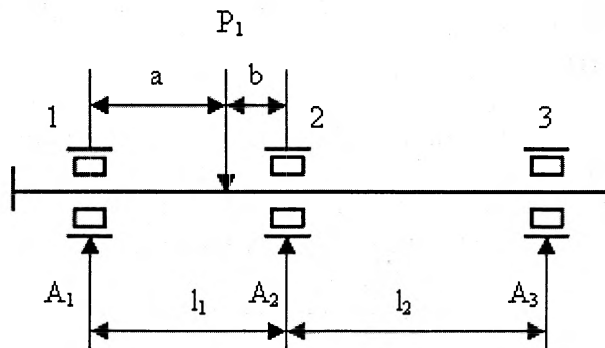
Схема нагружения трехопорного вала 1 коробки передач автомобиля БелАЗ
